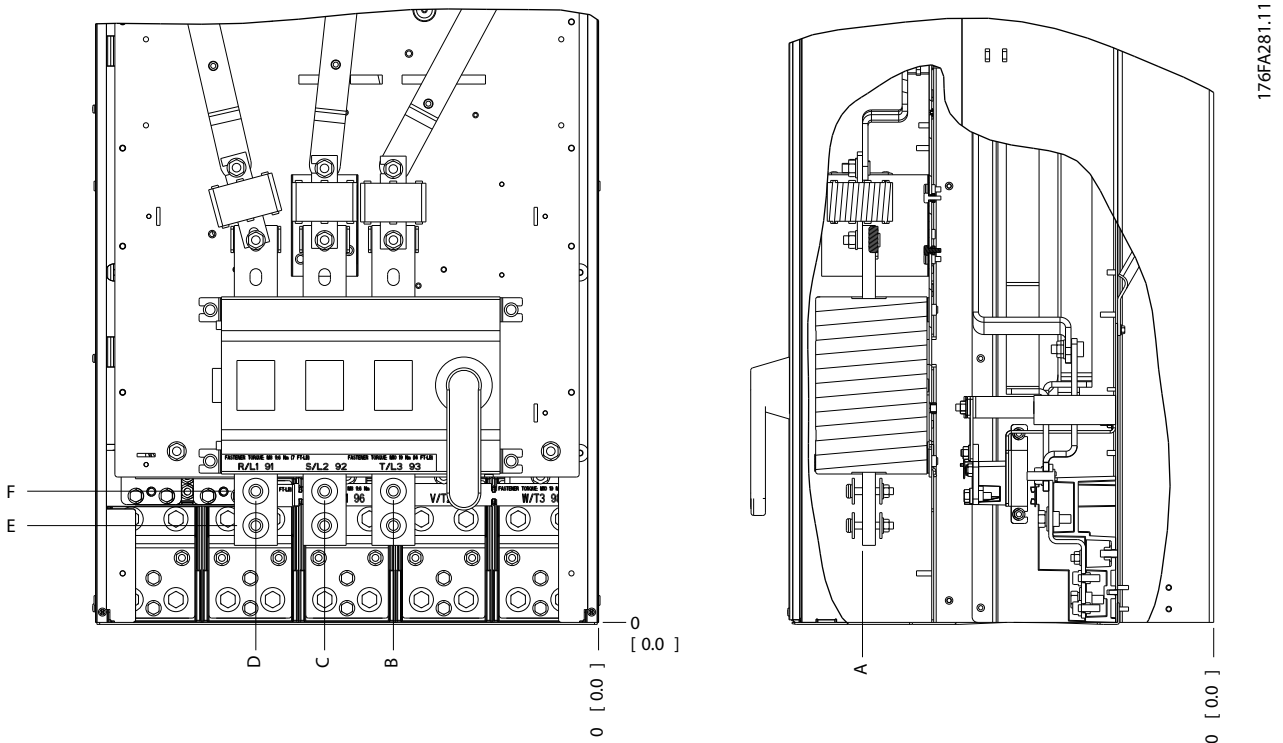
Расположение разъемов питания на корпусе IP00, расположение расцепителя
